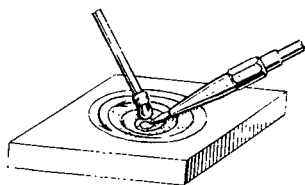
Положение прутка и горелки при заварке круглой разделки дефектов
